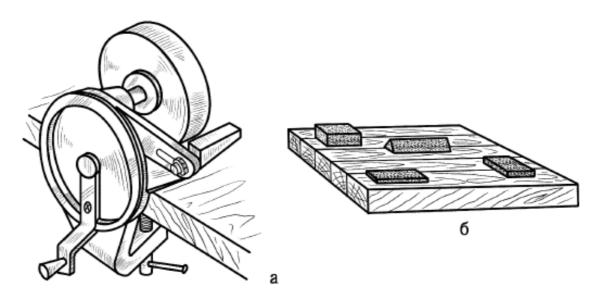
Инструмент и приспособление для заточки и правки режущего инструмента: a – ручное точило;  $\delta$  – щит с брусками и оселками
